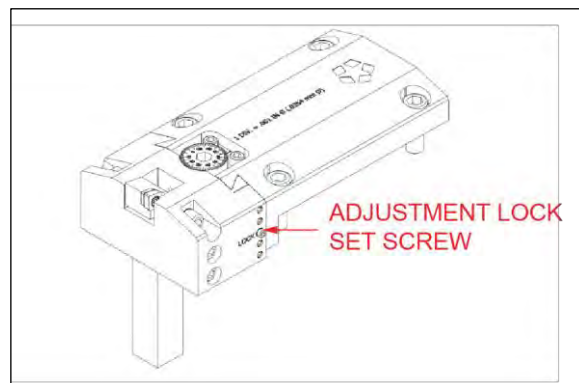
Расточная головка с функцией микрорегулировки и регулировочный стопорный установочный винт
